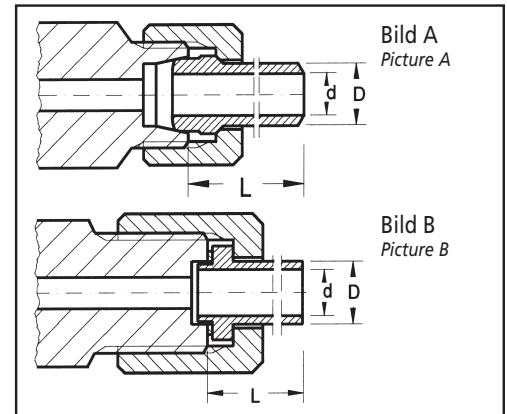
Bild A: Schweißkugelbuchse (PN400) (s. Kapitel Zubehör Seite Z3)
